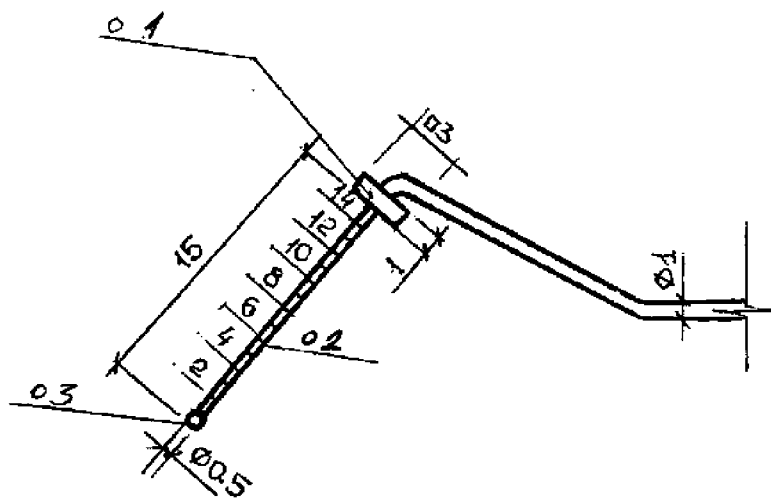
Схематичне зображення робочої частини пристрою для вимірювання глибини присінка рота М 2:1, 1 – гумовий обмежувач; 2 – градуйована частина пристрою; 3 – гудзикове закінчення.
